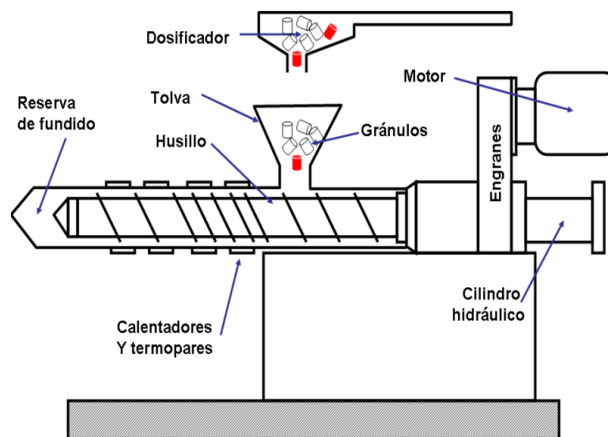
Diseño genérico de una unidad de moldeo por inyección [21]
